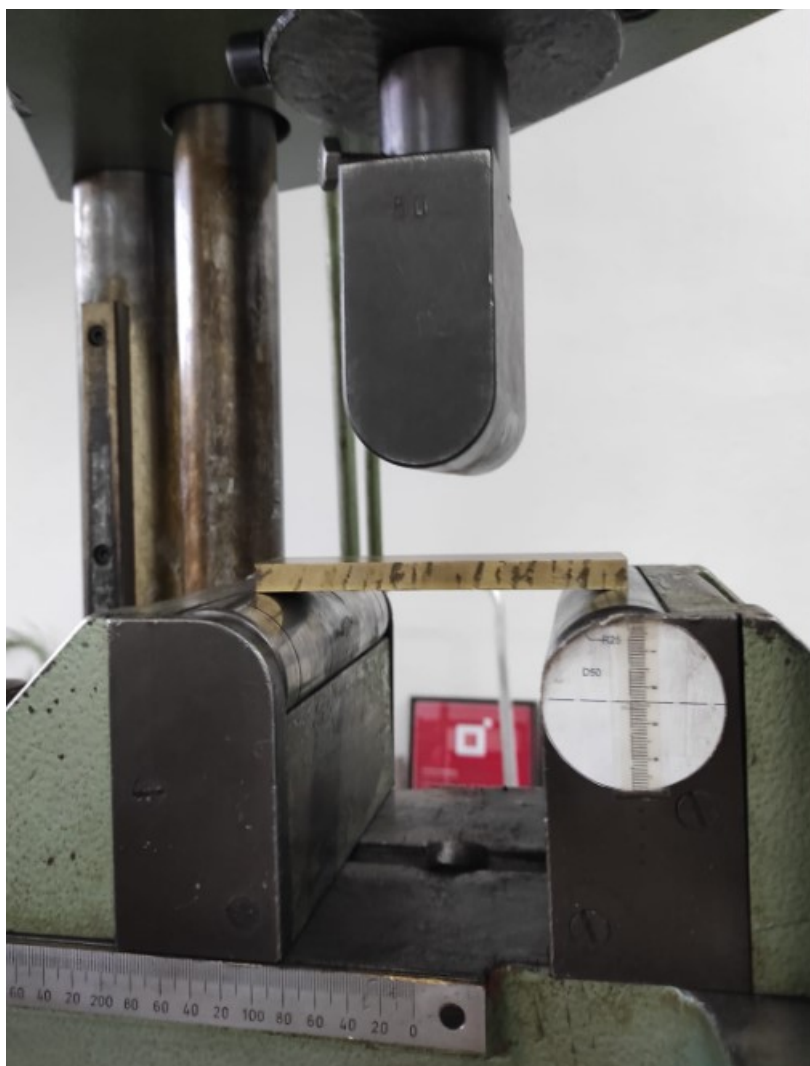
Longitudinalni test savijanja u korijenu zavara [19]
